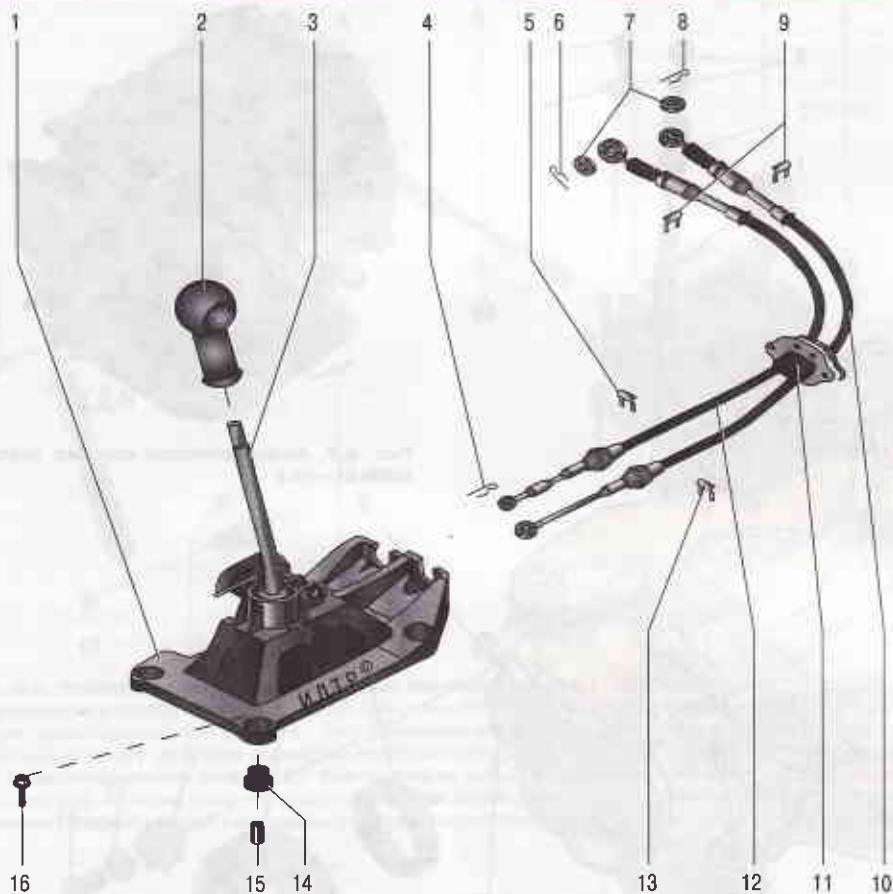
Привод управления коробкой передач Y4M: 1 – кулиса рычага управления коробкой передач; 2 – рукоятка рычага управления коробкой передач; 3 – рычаг управления коробкой передач; 4, 6, 8 – шплинты; 5, 9, 13 – скобы крепления тросов; 7 – шайбы; 10 – трос выбора передач; 11 – держатель тросов; 12 – трос переключения передач; 14 – демпферная втулка; 15 – распорная втулка; 16 – болт крепления кулисы
